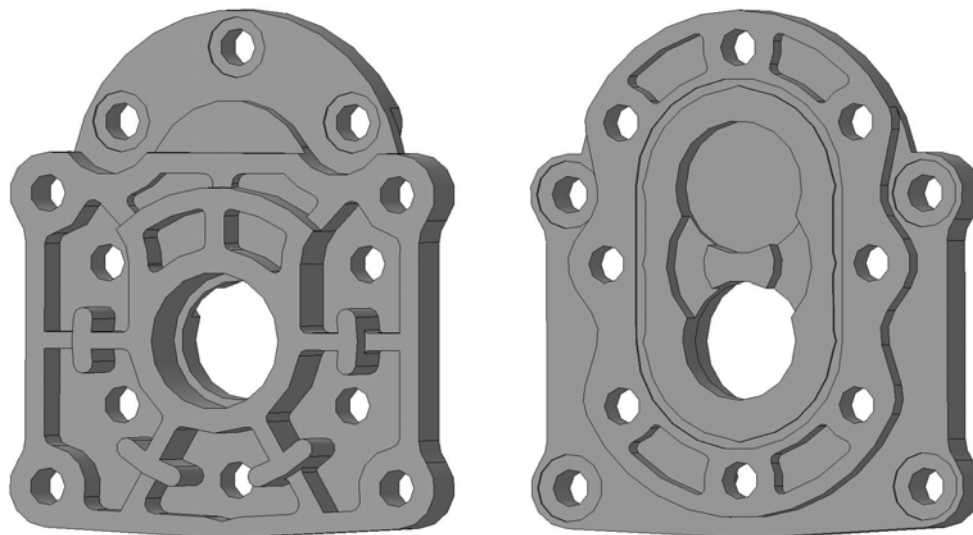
3D-модель виливка деталі «Кришка насоса НШ32.У» при литті під тиском
